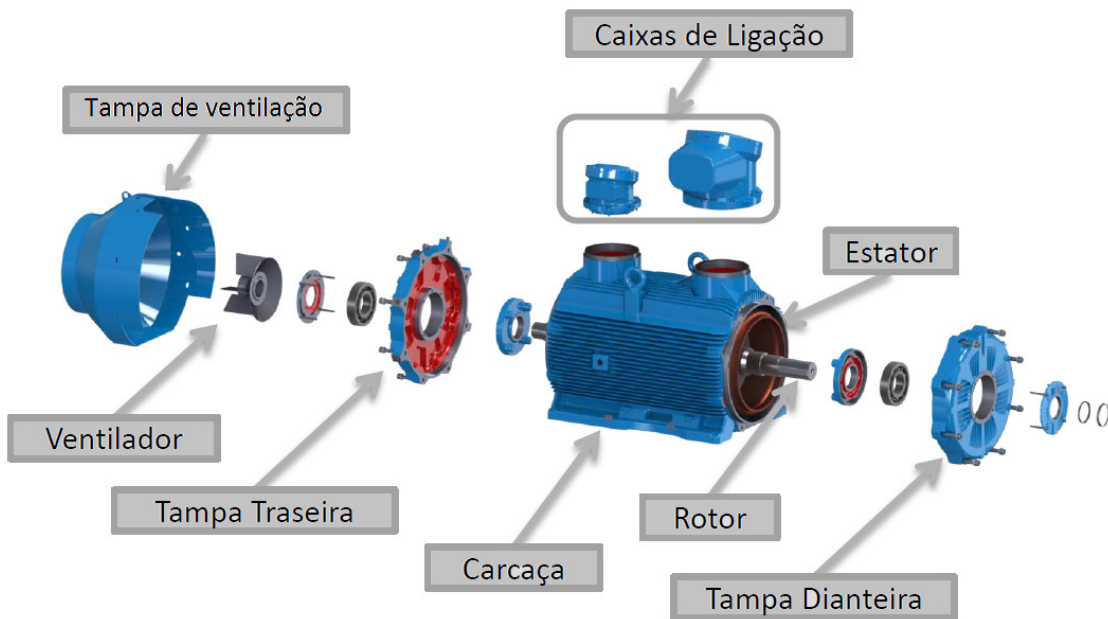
Vista explodida de motor W22X. Fonte: Cortesia WEG
